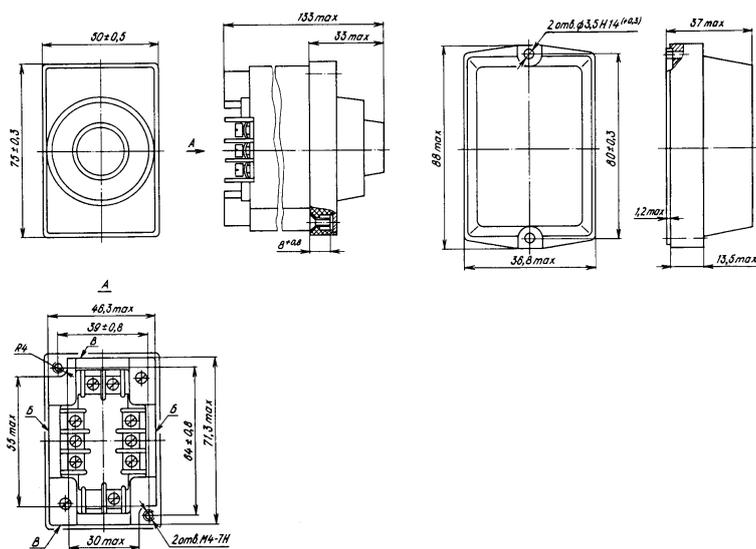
Габаритные и установочные размеры и крепление реле ВС-33-2
